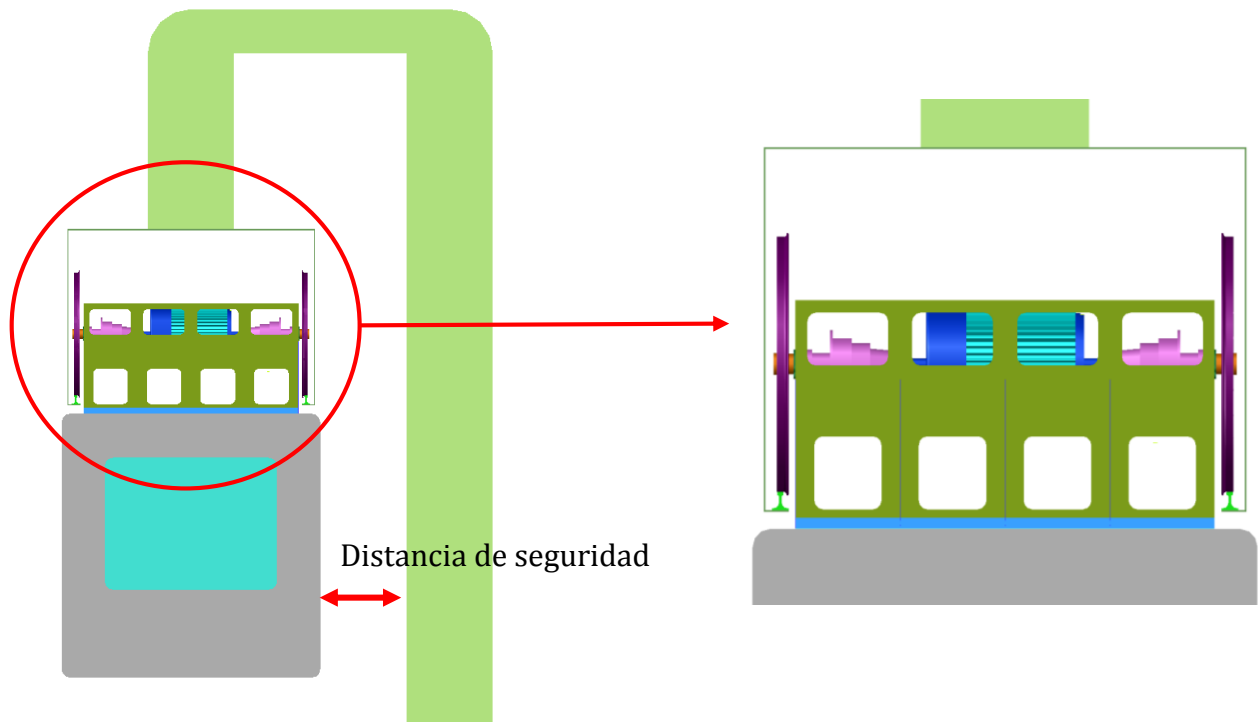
Detalle de la distancia entre el coche y la infraestructura.
